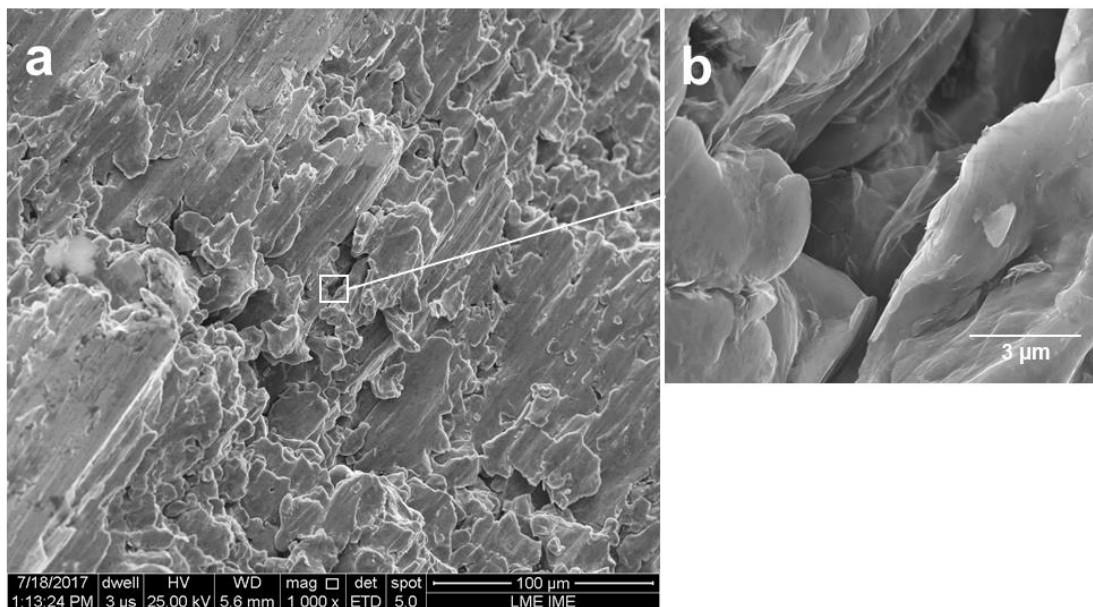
Superfície de fratura referente a composição Cu-1,0%TrGO com aumentos de (a) 1000x e (b) 25000x.
